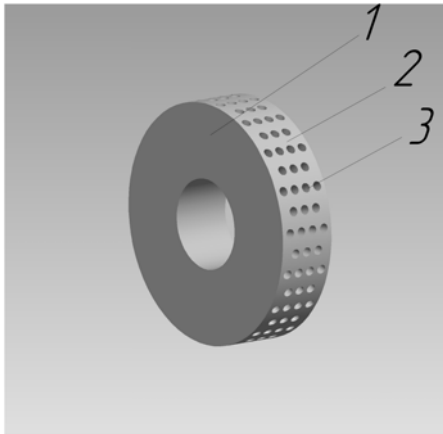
Шлифовальный круг с лазерной дискретизацией
